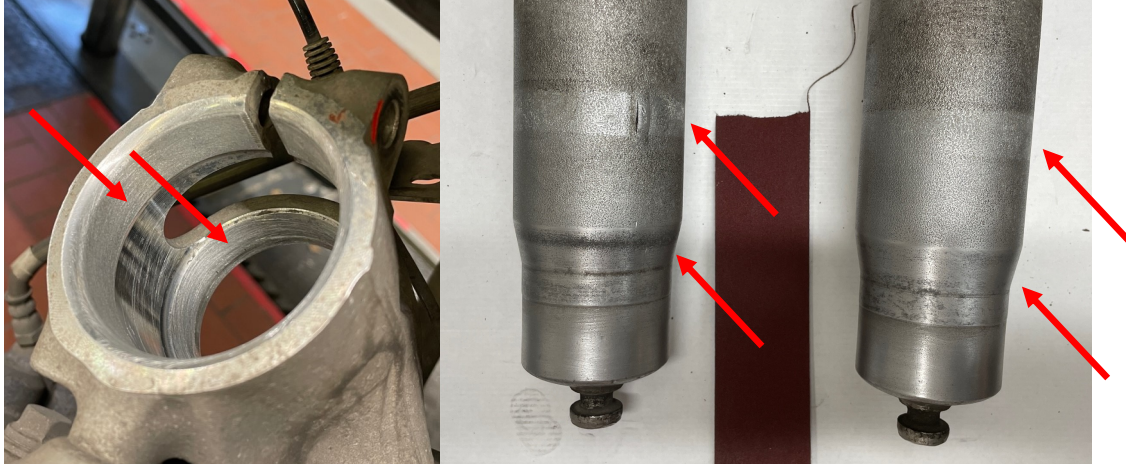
Anlageflächen mit Schleifpapier reinigen/anrauen
